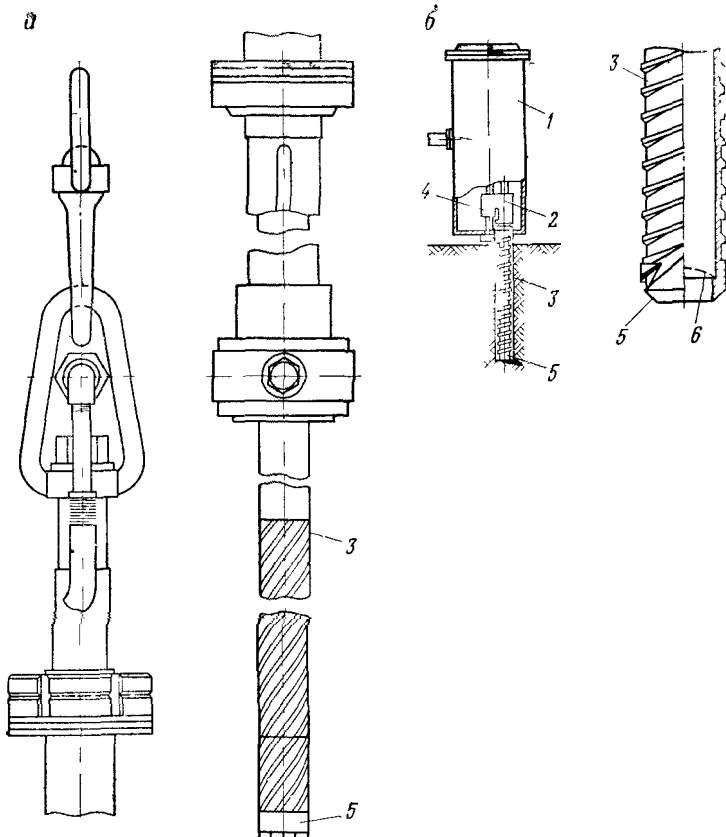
Ленточная труба (а) бурового станка начала XX в. и шнековая труба (б) бурового устройства автоматической межпланетной станции «Луна-16»: 1 — корпус; 2 — вращатель; 3 — шнековая колонковая труба; 4 — винт подачи; 5 — коронка; 6 — кернорватель
